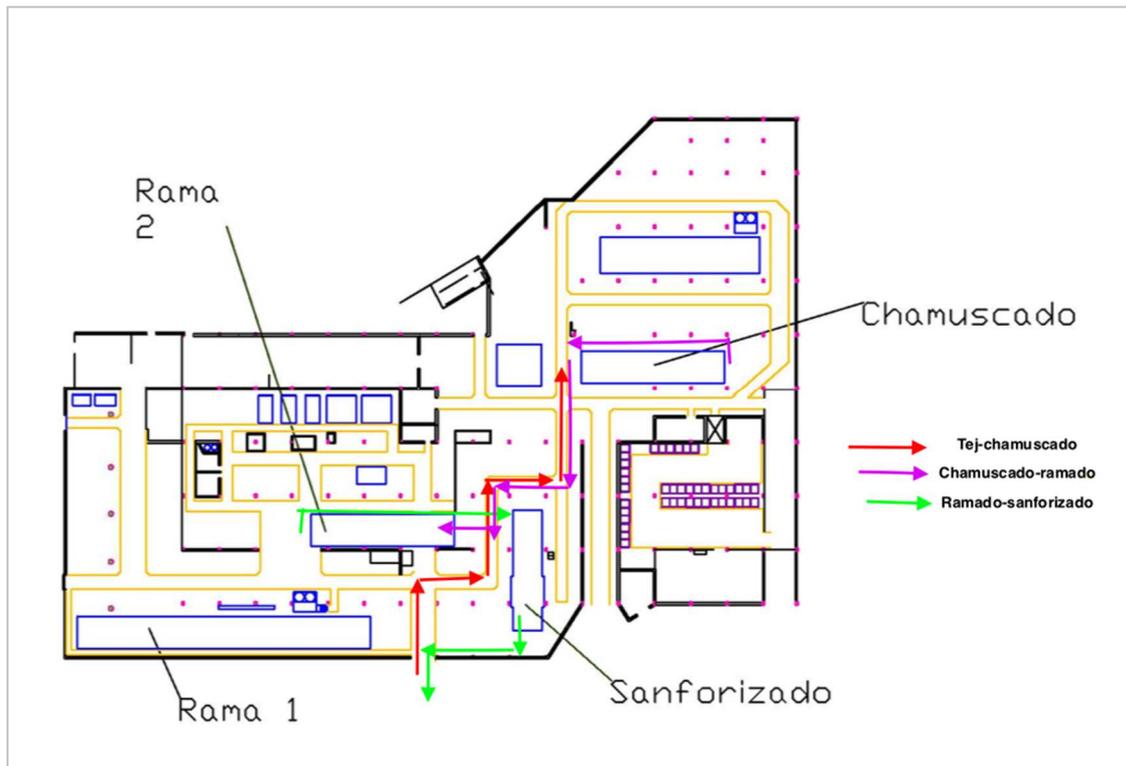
Layout actual del Sector de Terminación. (Diforti, 2018)
